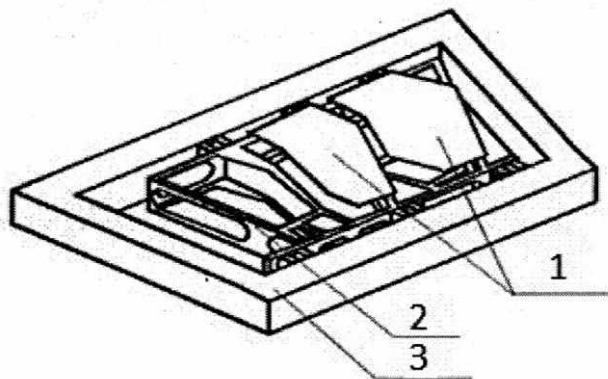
Условие закрепления сварной авиационной конструкции:
